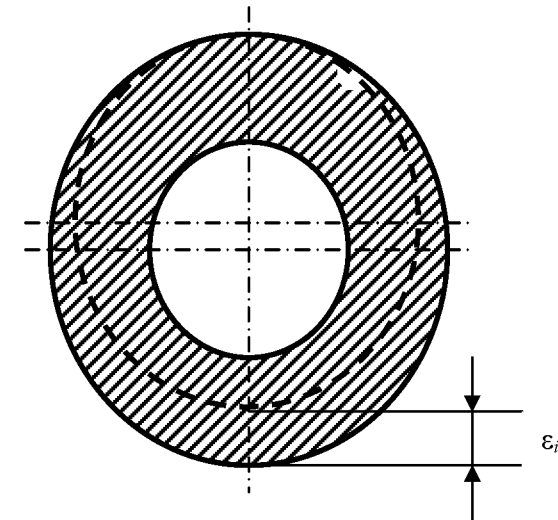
Смещение обрабатываемой поверхности относительно базовой  $\epsilon_i$ , происходящее при обработке заготовки из-за неточности ее установки на оправке
